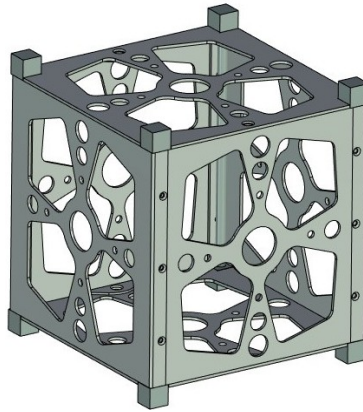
3D-модель корпуса для печати на 3D-принтере
